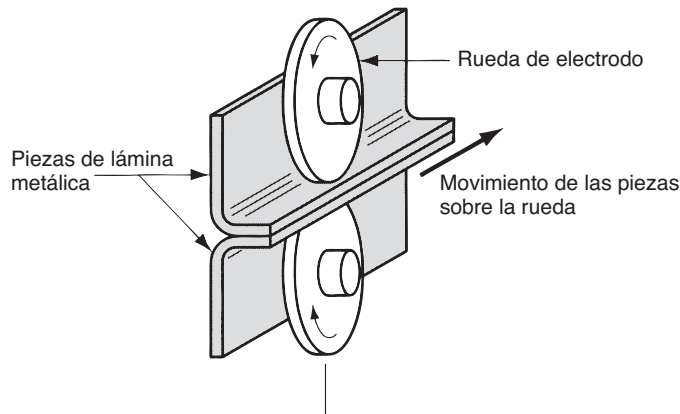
Soldadura de costura por resistencia (RSEW).
